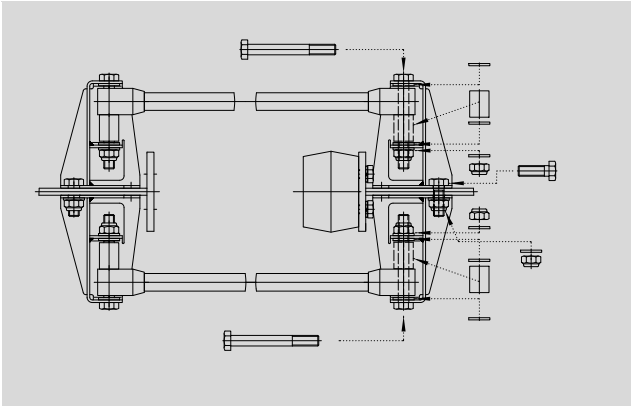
Dämpfungseinrichtung mit 2 Gummiseilen, für Haupttragrollen \varnothing 80, 100, 112, 125 und 160 mm
